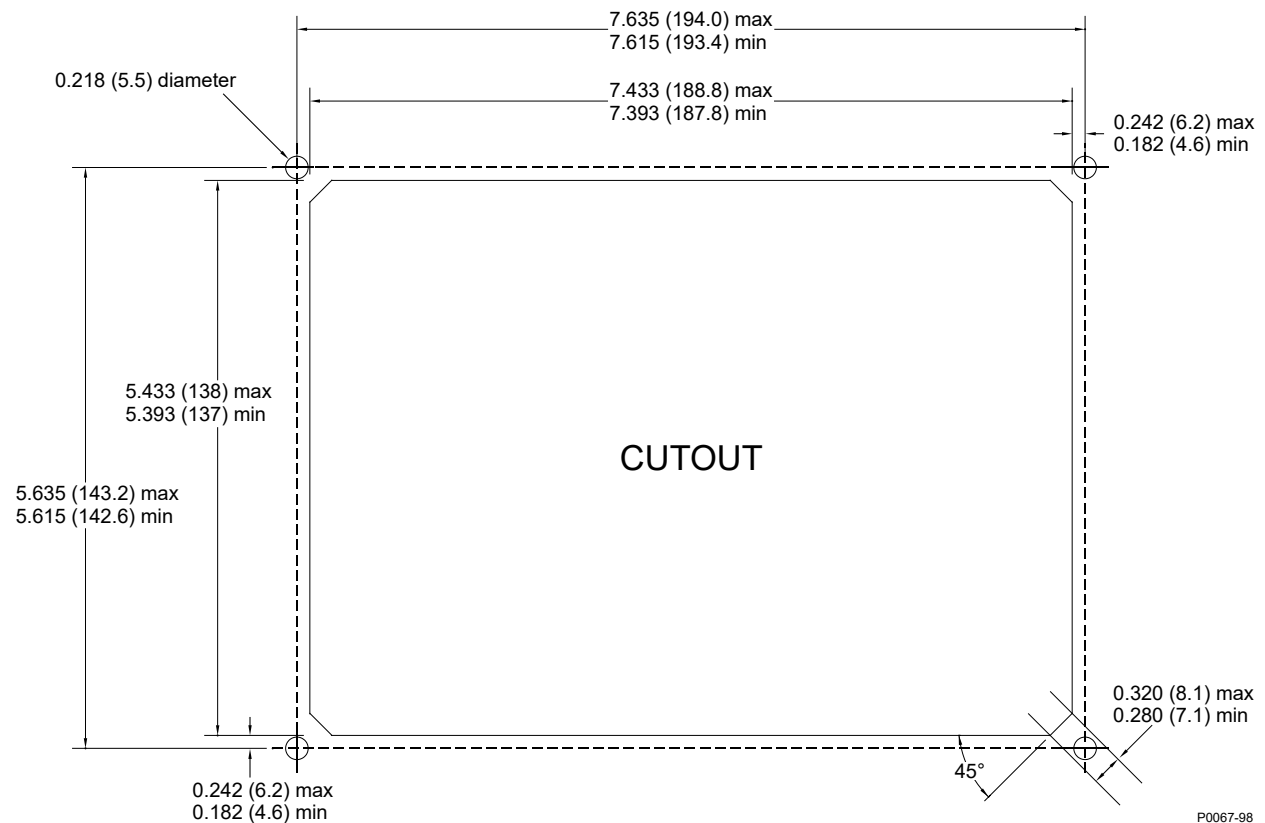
Calado de Panel y Dimensiones de Perforación
